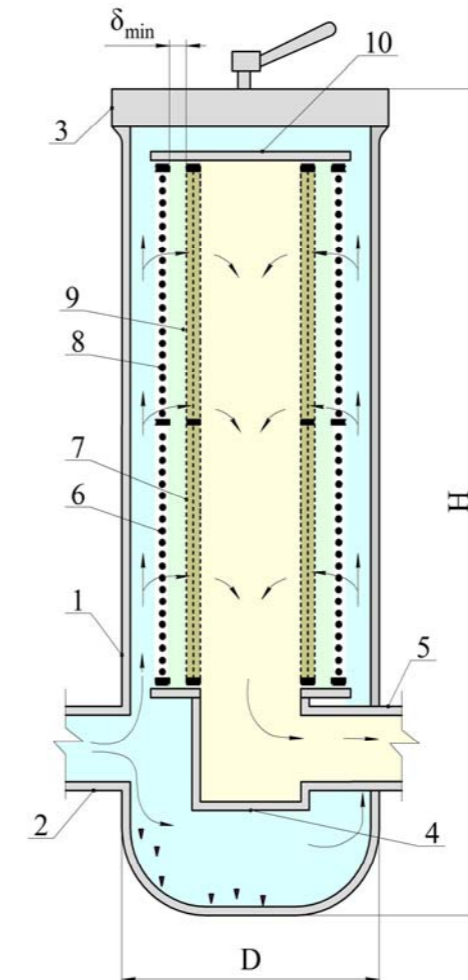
Двухступенчатая установка с ЦФЭ предварительной и тонкой очистки, размещенными в одном корпусе:
